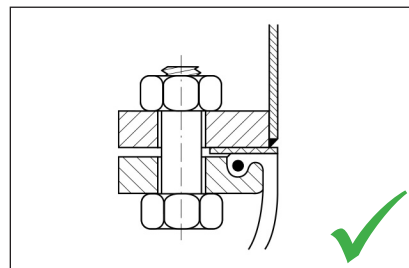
Flansch mit zusätzlicher flacher Dichtung zum Schutz des Gummis.
